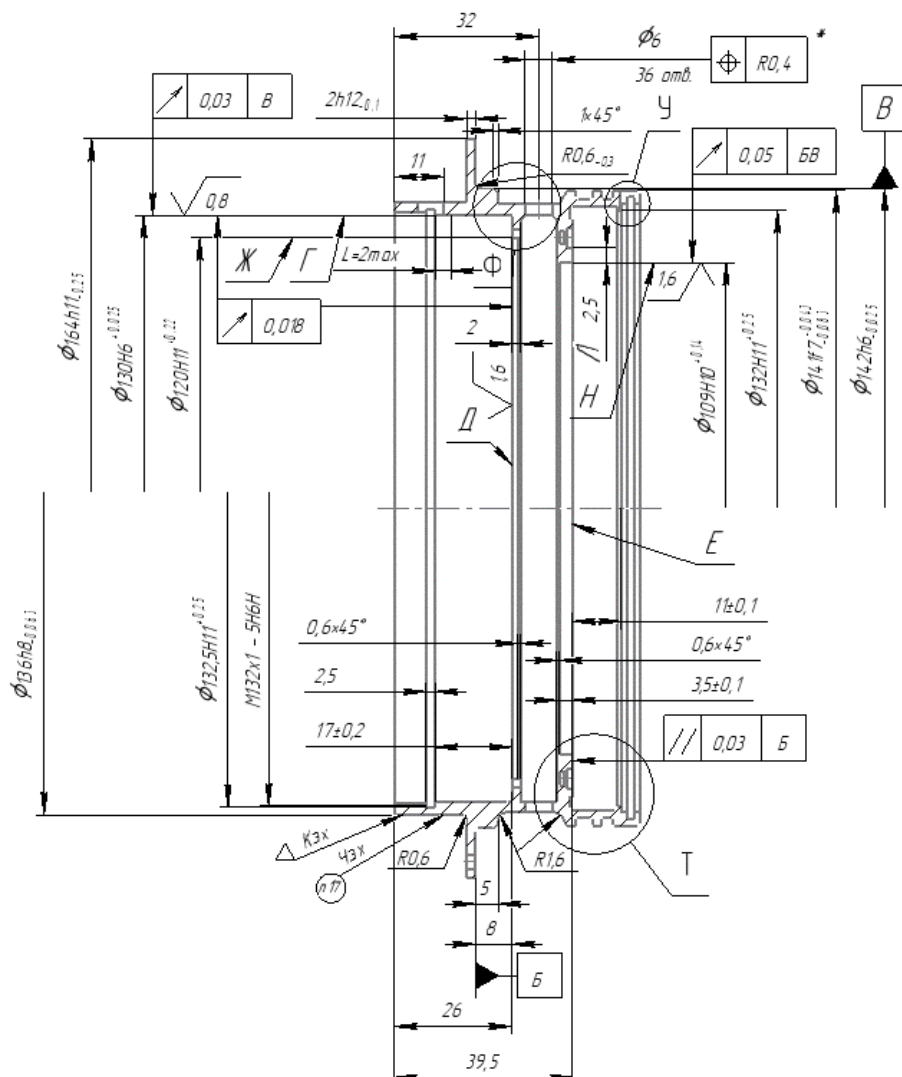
Чертеж детали «Корпус роликоподшипника»
